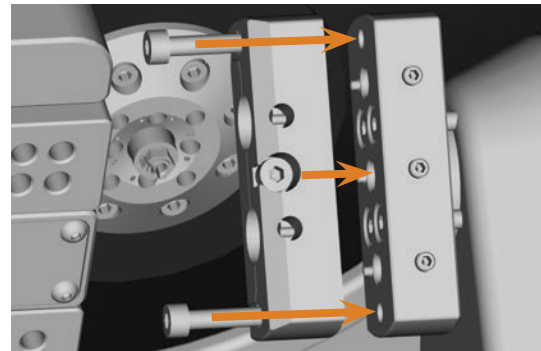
ABUTMENTHALTER ANSCHRAUBEN
